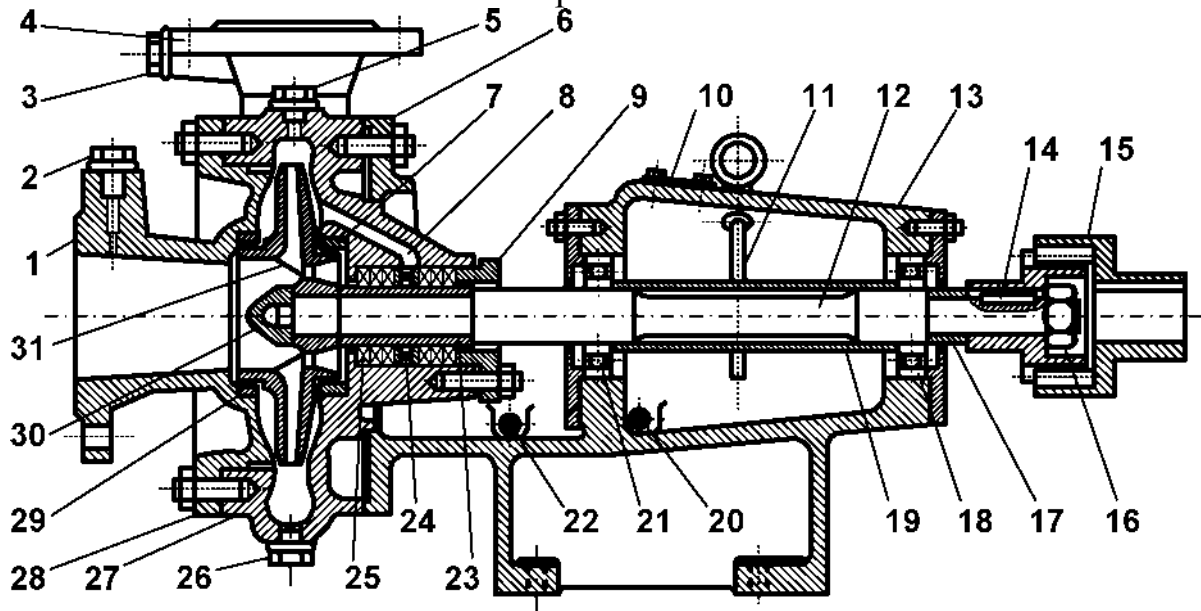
Консольный насос типа К: 1 и 4 - всасывающий и нагнетательный патрубки; 2 и 3 - гнезда для установки вакуумметра и манометра; 5 и 26 - верхняя и нижняя пробки корпуса; 6 - опорный фланец для корпуса насоса; 7 и 29 - кольцевые уплотняющие втулки; 8 - канал гидрозатвора сальника; 9 - фланец сальника; 10 - крышка камеры подшипников; 11 - щуп; 12 - вал; 13 - камера подшипников; 14 - шпонка; 15 - соединительная муфта; 16 - стопорная гайка полумуфты; 17 и 19 - дистанционные втулки; 18 - задний радиально-упорный подшипник; 20 - сливное отверстие для масла; 21 - передний радиальный подшипник; 22 - дренажное отверстие; 23 - защитная втулка; 24 - водораспределительная втулка; 25 - сальниковая набивка; 27 - корпус насоса; 28 - передний щит; 30 - стопорная гайка рабочего колеса; 31 - рабочее колесо
